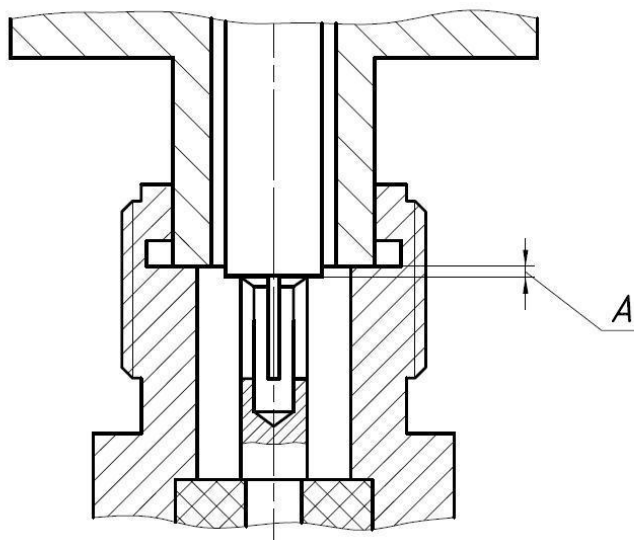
Проверка размера «А» соединителя «розетка»
